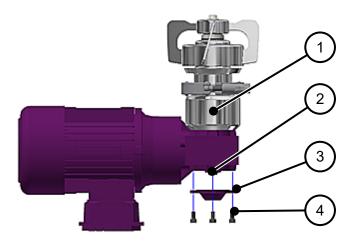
Maschine mit Abdeckhaube (Explosionsdarstellung)
